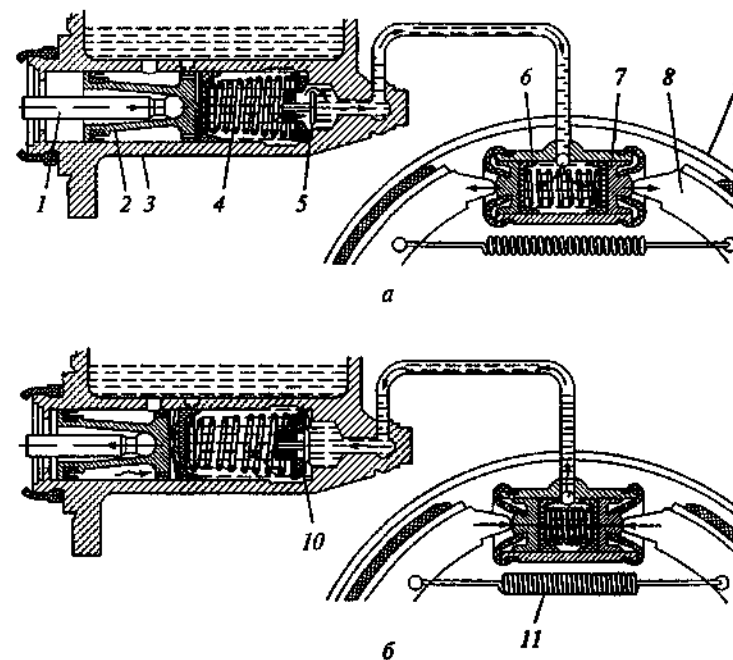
Схема работы гидравлического тормозного привода: *а* — торможение; *б* — растормаживание; / — толкатель; 2 и 7 — поршни; 3 и 6 — цилиндры; 4 и 11 — пружины; 5 и 10 — клапаны; 8 — колодка; 9 — тормозной барабан
